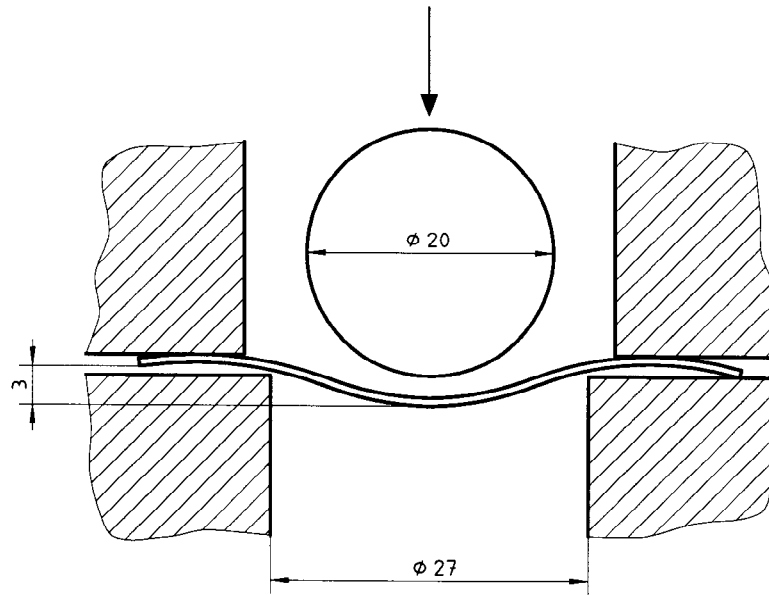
Dimensions de la bille, de la matrice et du serre-flan
